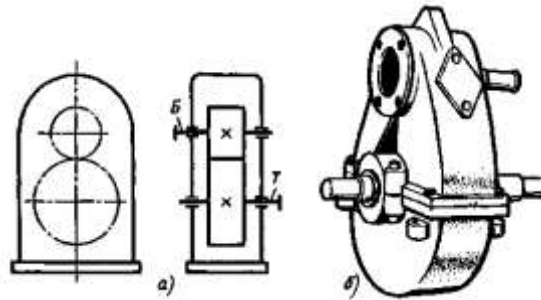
Одноступенчатый вертикальный редуктор с цилиндрическими колесами:
